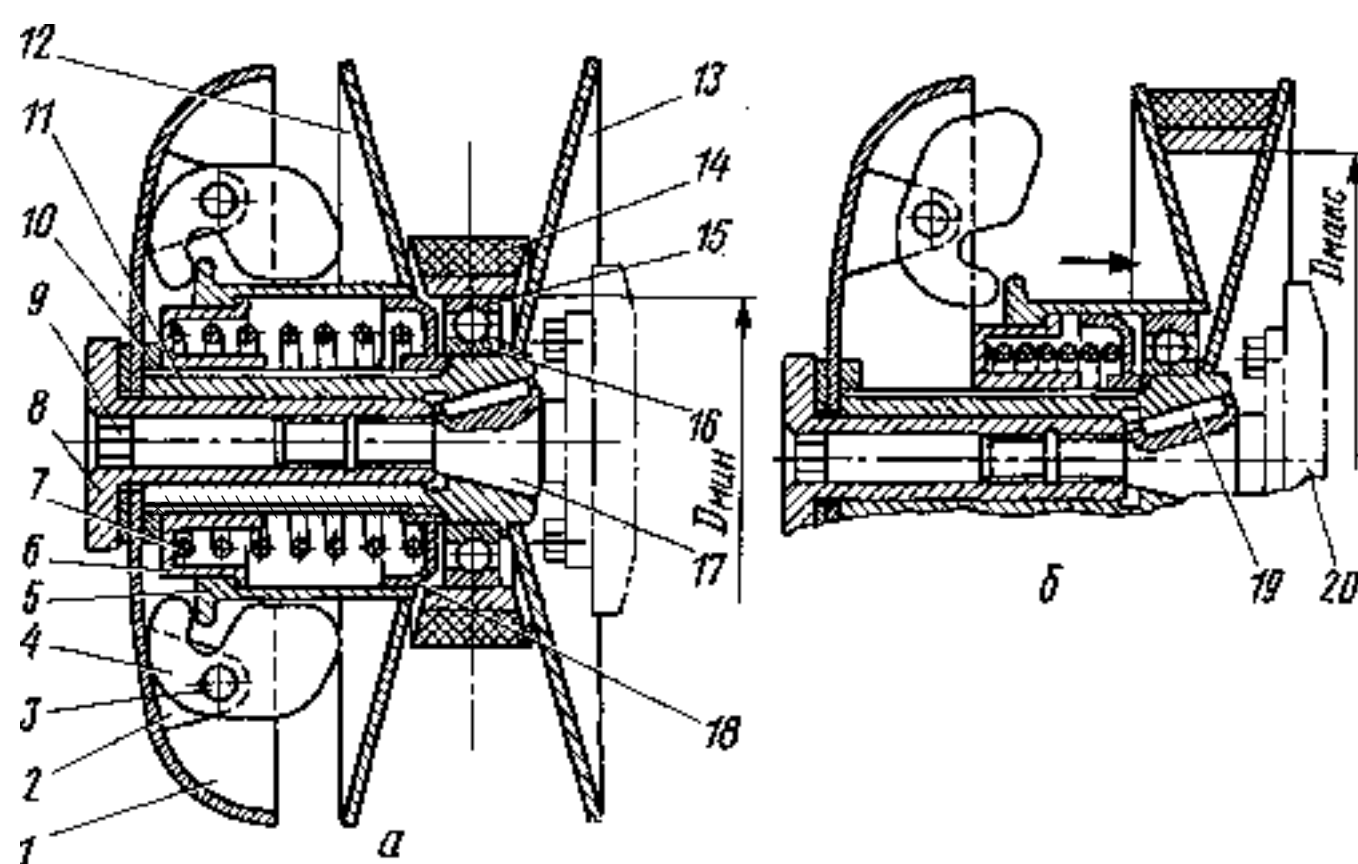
Конструктивная схема ведущего шкива вариатора:
